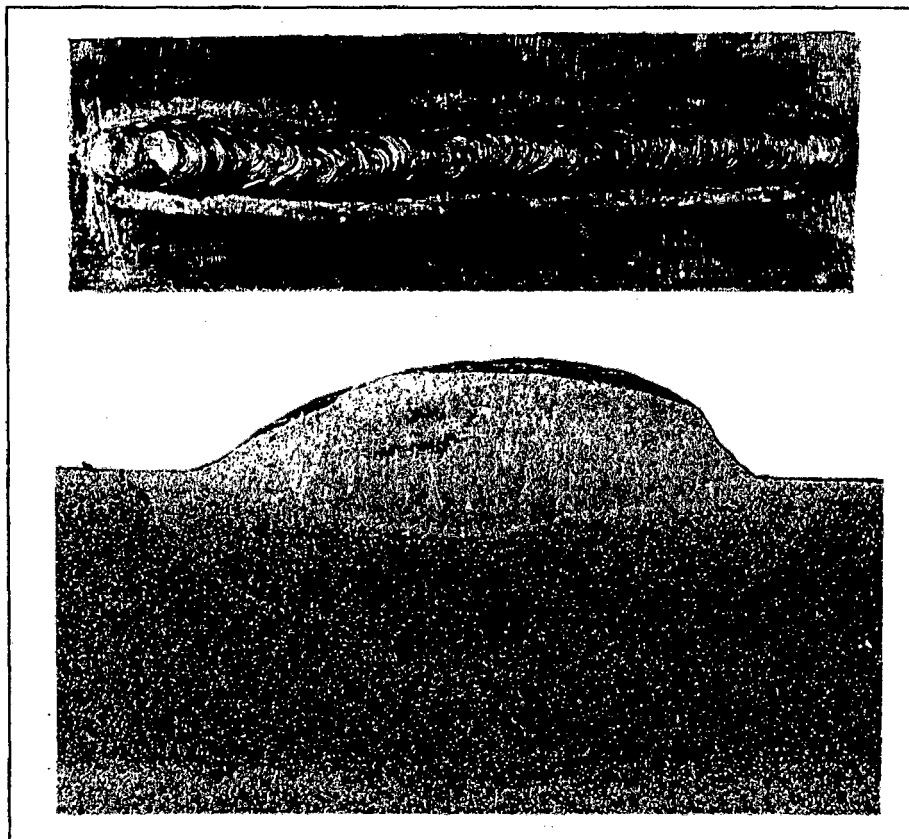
Aspecto do cordão de solda para o eletrodo H em CA.
